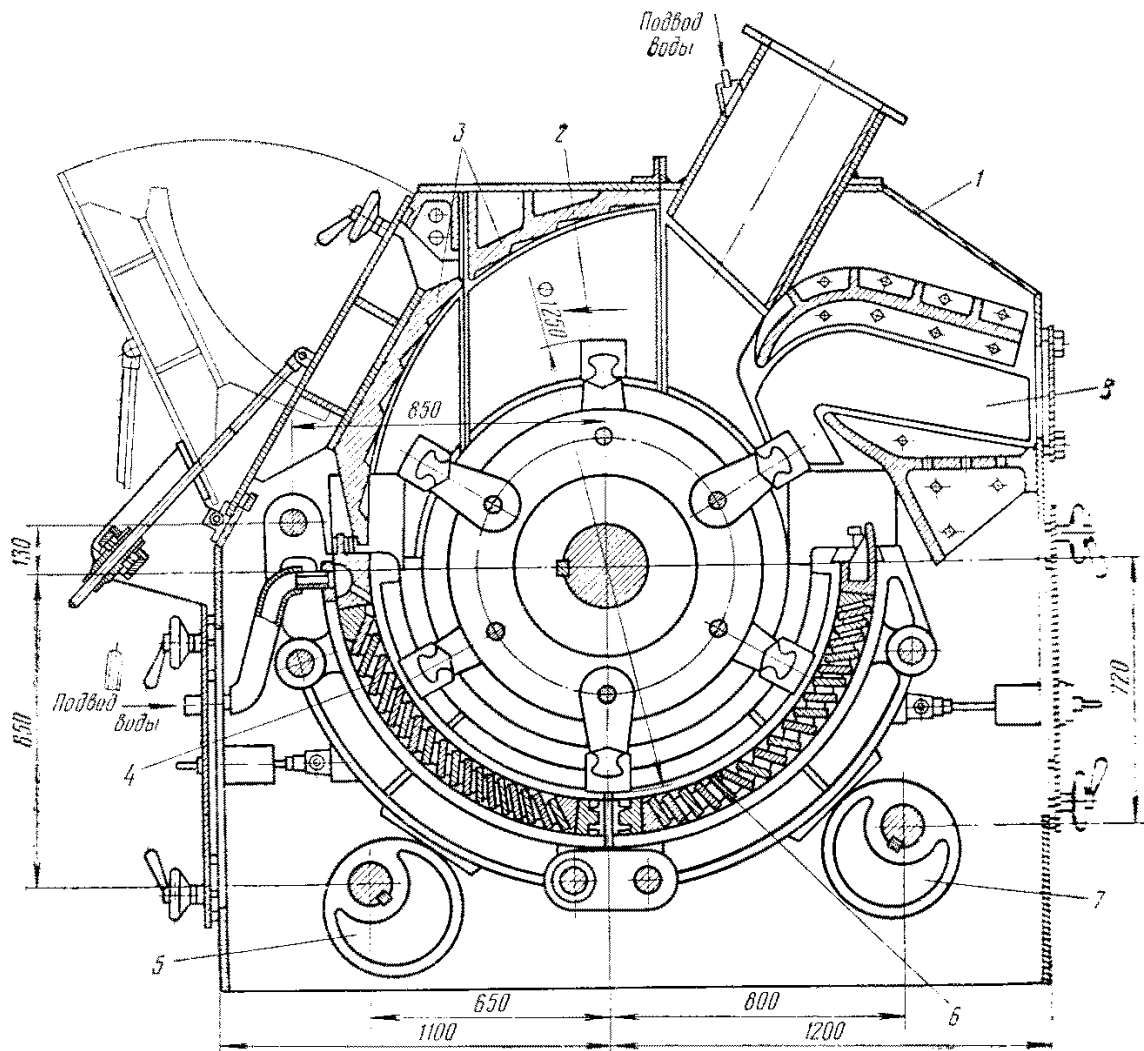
Схема однороторної нереверсивної молоткової дробарки:
